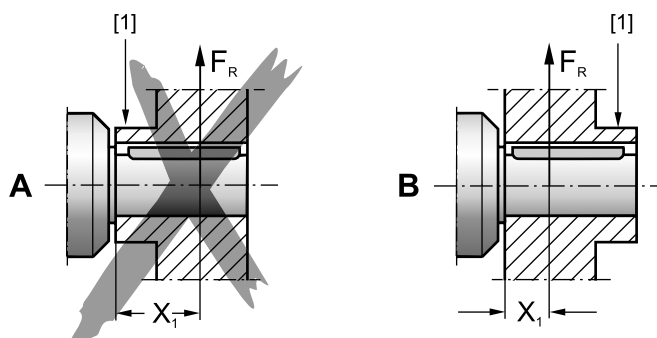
Disposição de montagem correcta de uma polia ou roda dentada
